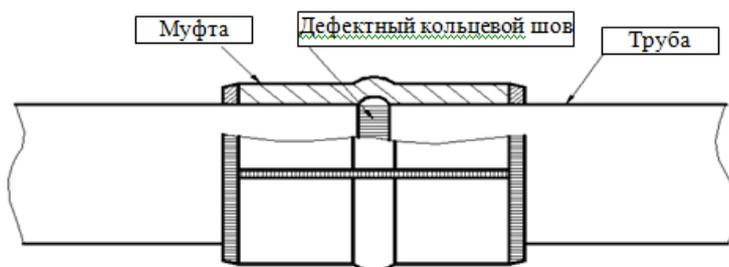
Муфта типа ПЗ галтельная для ремонта сварных кольцевых швов
